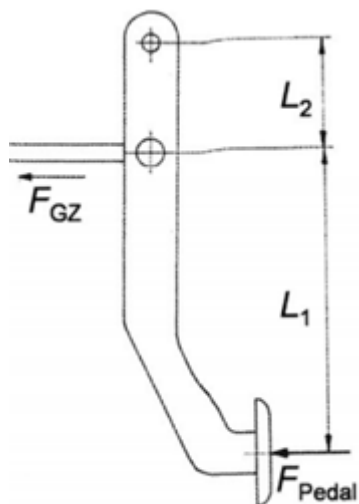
Hydraulické ovládání a mechanismus spojky - převzato z [i1]
